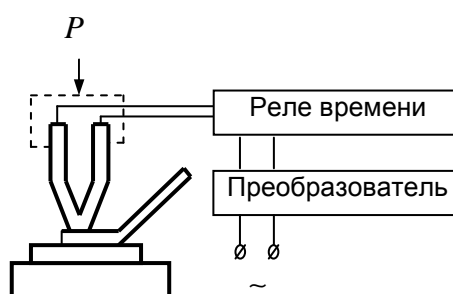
Схема сварки давлением с косвенным импульсным нагревом
